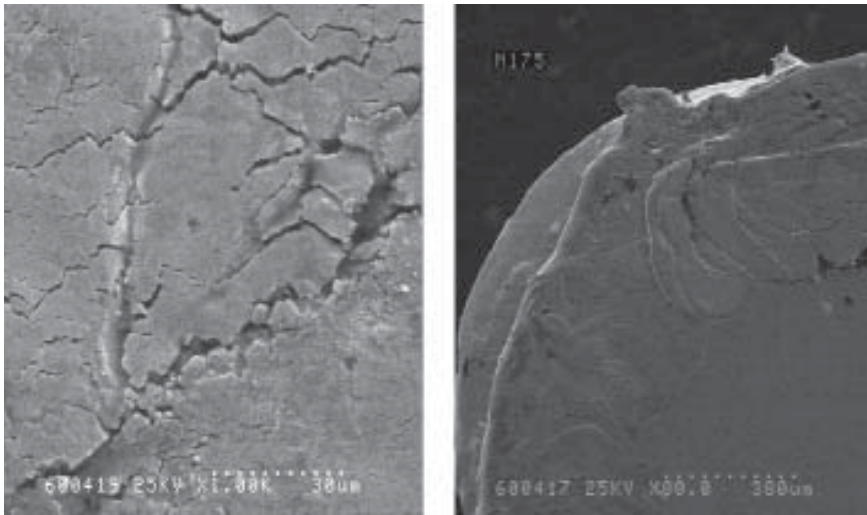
Внешний вид сварного шва на поверхности крышки корпуса
